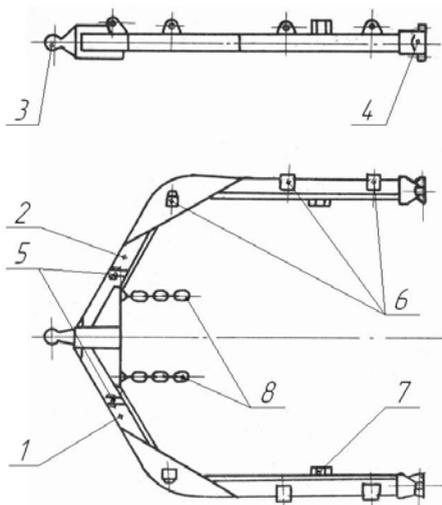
Рама универсальная: 1, 2 – брусья толкающие; 3 – опора шаровая; 4 – шарниры соединительные; 5 – кронштейны для гидроцилиндров подъема-опускания; 6 – кронштейны винтовых раскосов; 7 – буфер; 8 – цепи фиксирующие
